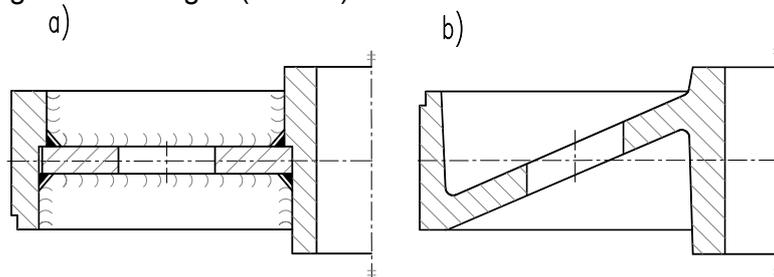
Geometrische Konstruktionsgestalten der Zahnradgehäuse
